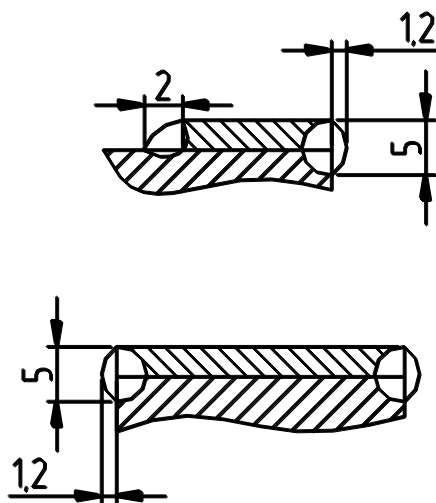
Сварные швы прокладок на вилках
